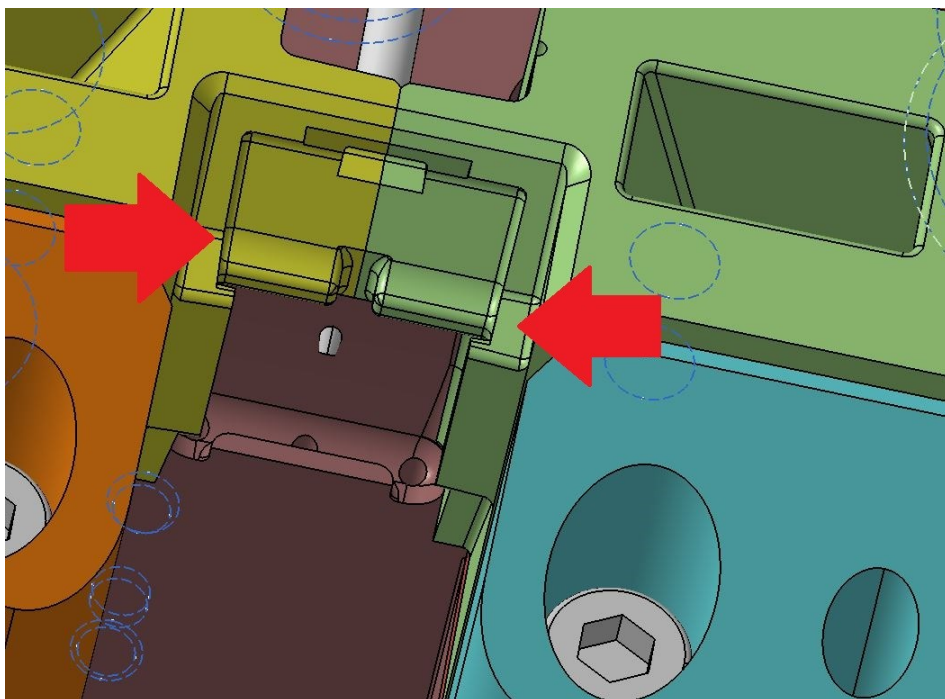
Hotový výrobek se zácvakem s hloubenými tvary elektrodami 3 a 4
